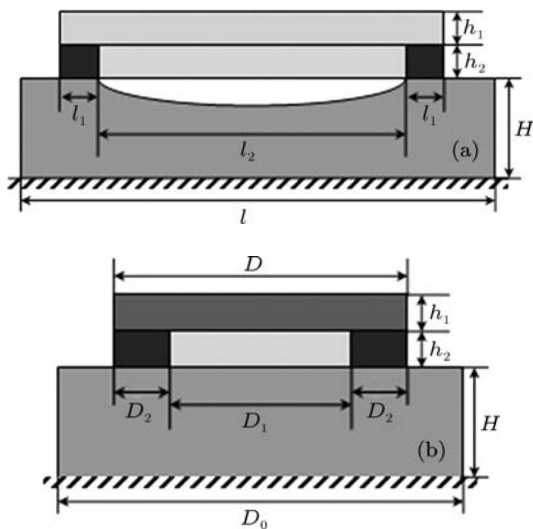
隔振器平面图 (a) YZ 平面图; (b) XZ 平面图
